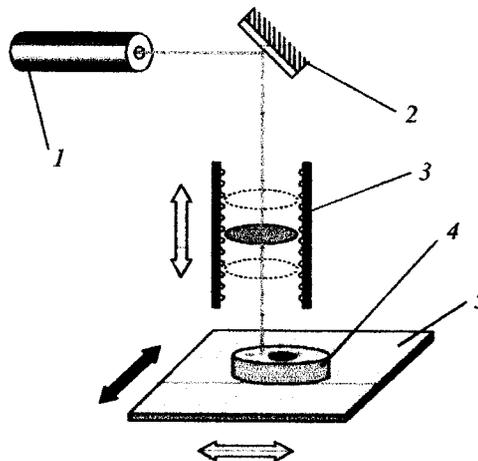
Схема реализации процесса лазерной обработки матриц аппаратов высокого давления: 1 – лазер; 2 – поворотное зеркало; 3 – механизм фокусировки; 4 – обрабатываемая матрица; 5 – координатный стол.
